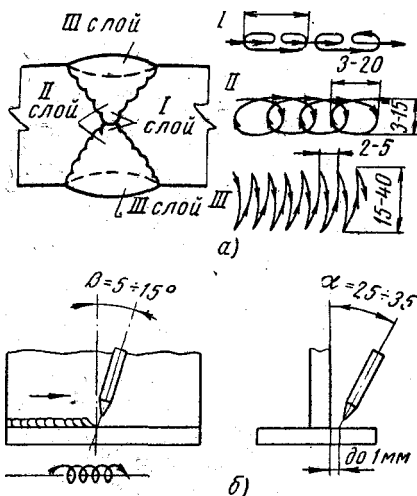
Перемещение конца проволоки при сварке в углекислом газе:
